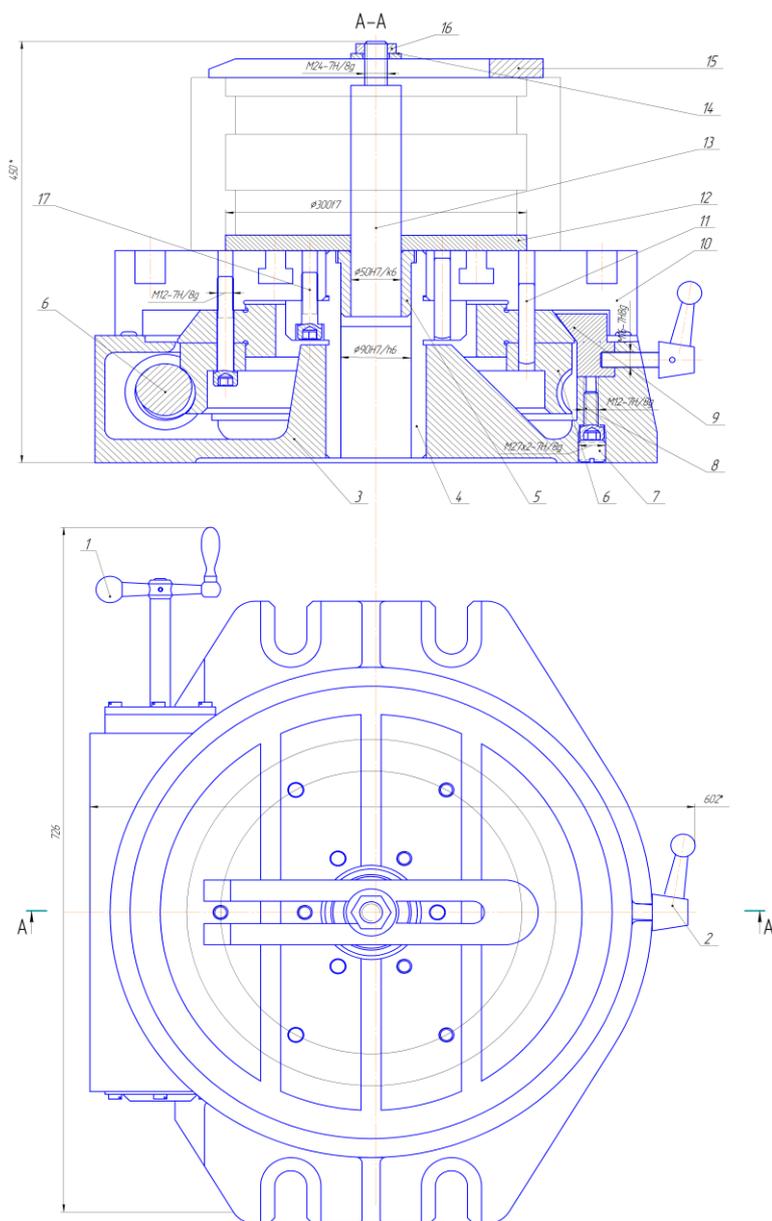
Эскиз приспособления поворотного (делительного) приспособления
